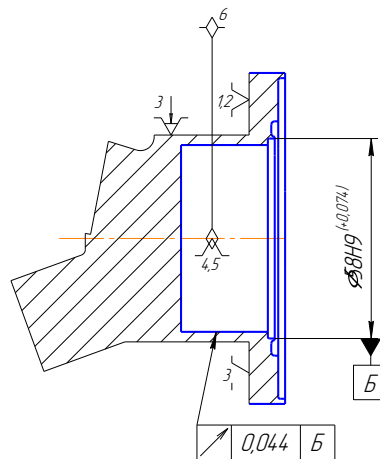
Схема базирования и установки детали «Крышка».
